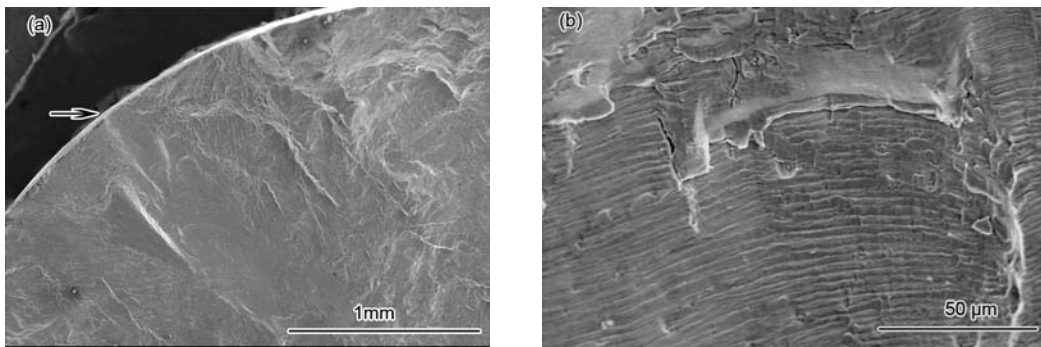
Inconel 625 合金焊接接头在 25 °C 下的低周疲劳裂纹萌生和扩展区的形貌
